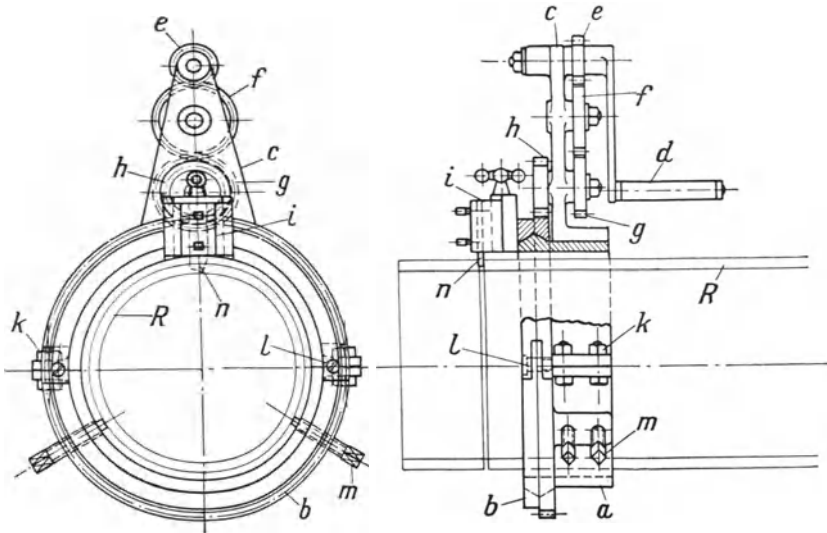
Rohrabschneidevorrichtung starker Gußrohrleitungen auf Montagen.
